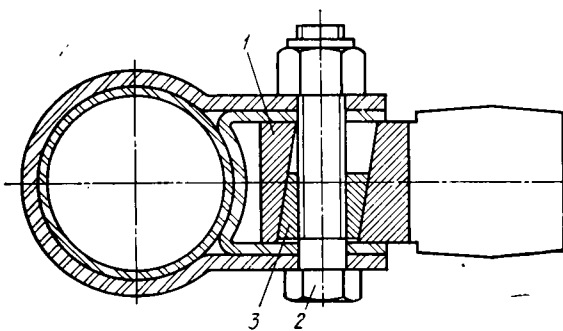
Узел регулировки угла развала передних колес: 1 — поворотный кулак; 2 — болт; 3 — гайка-ползун
